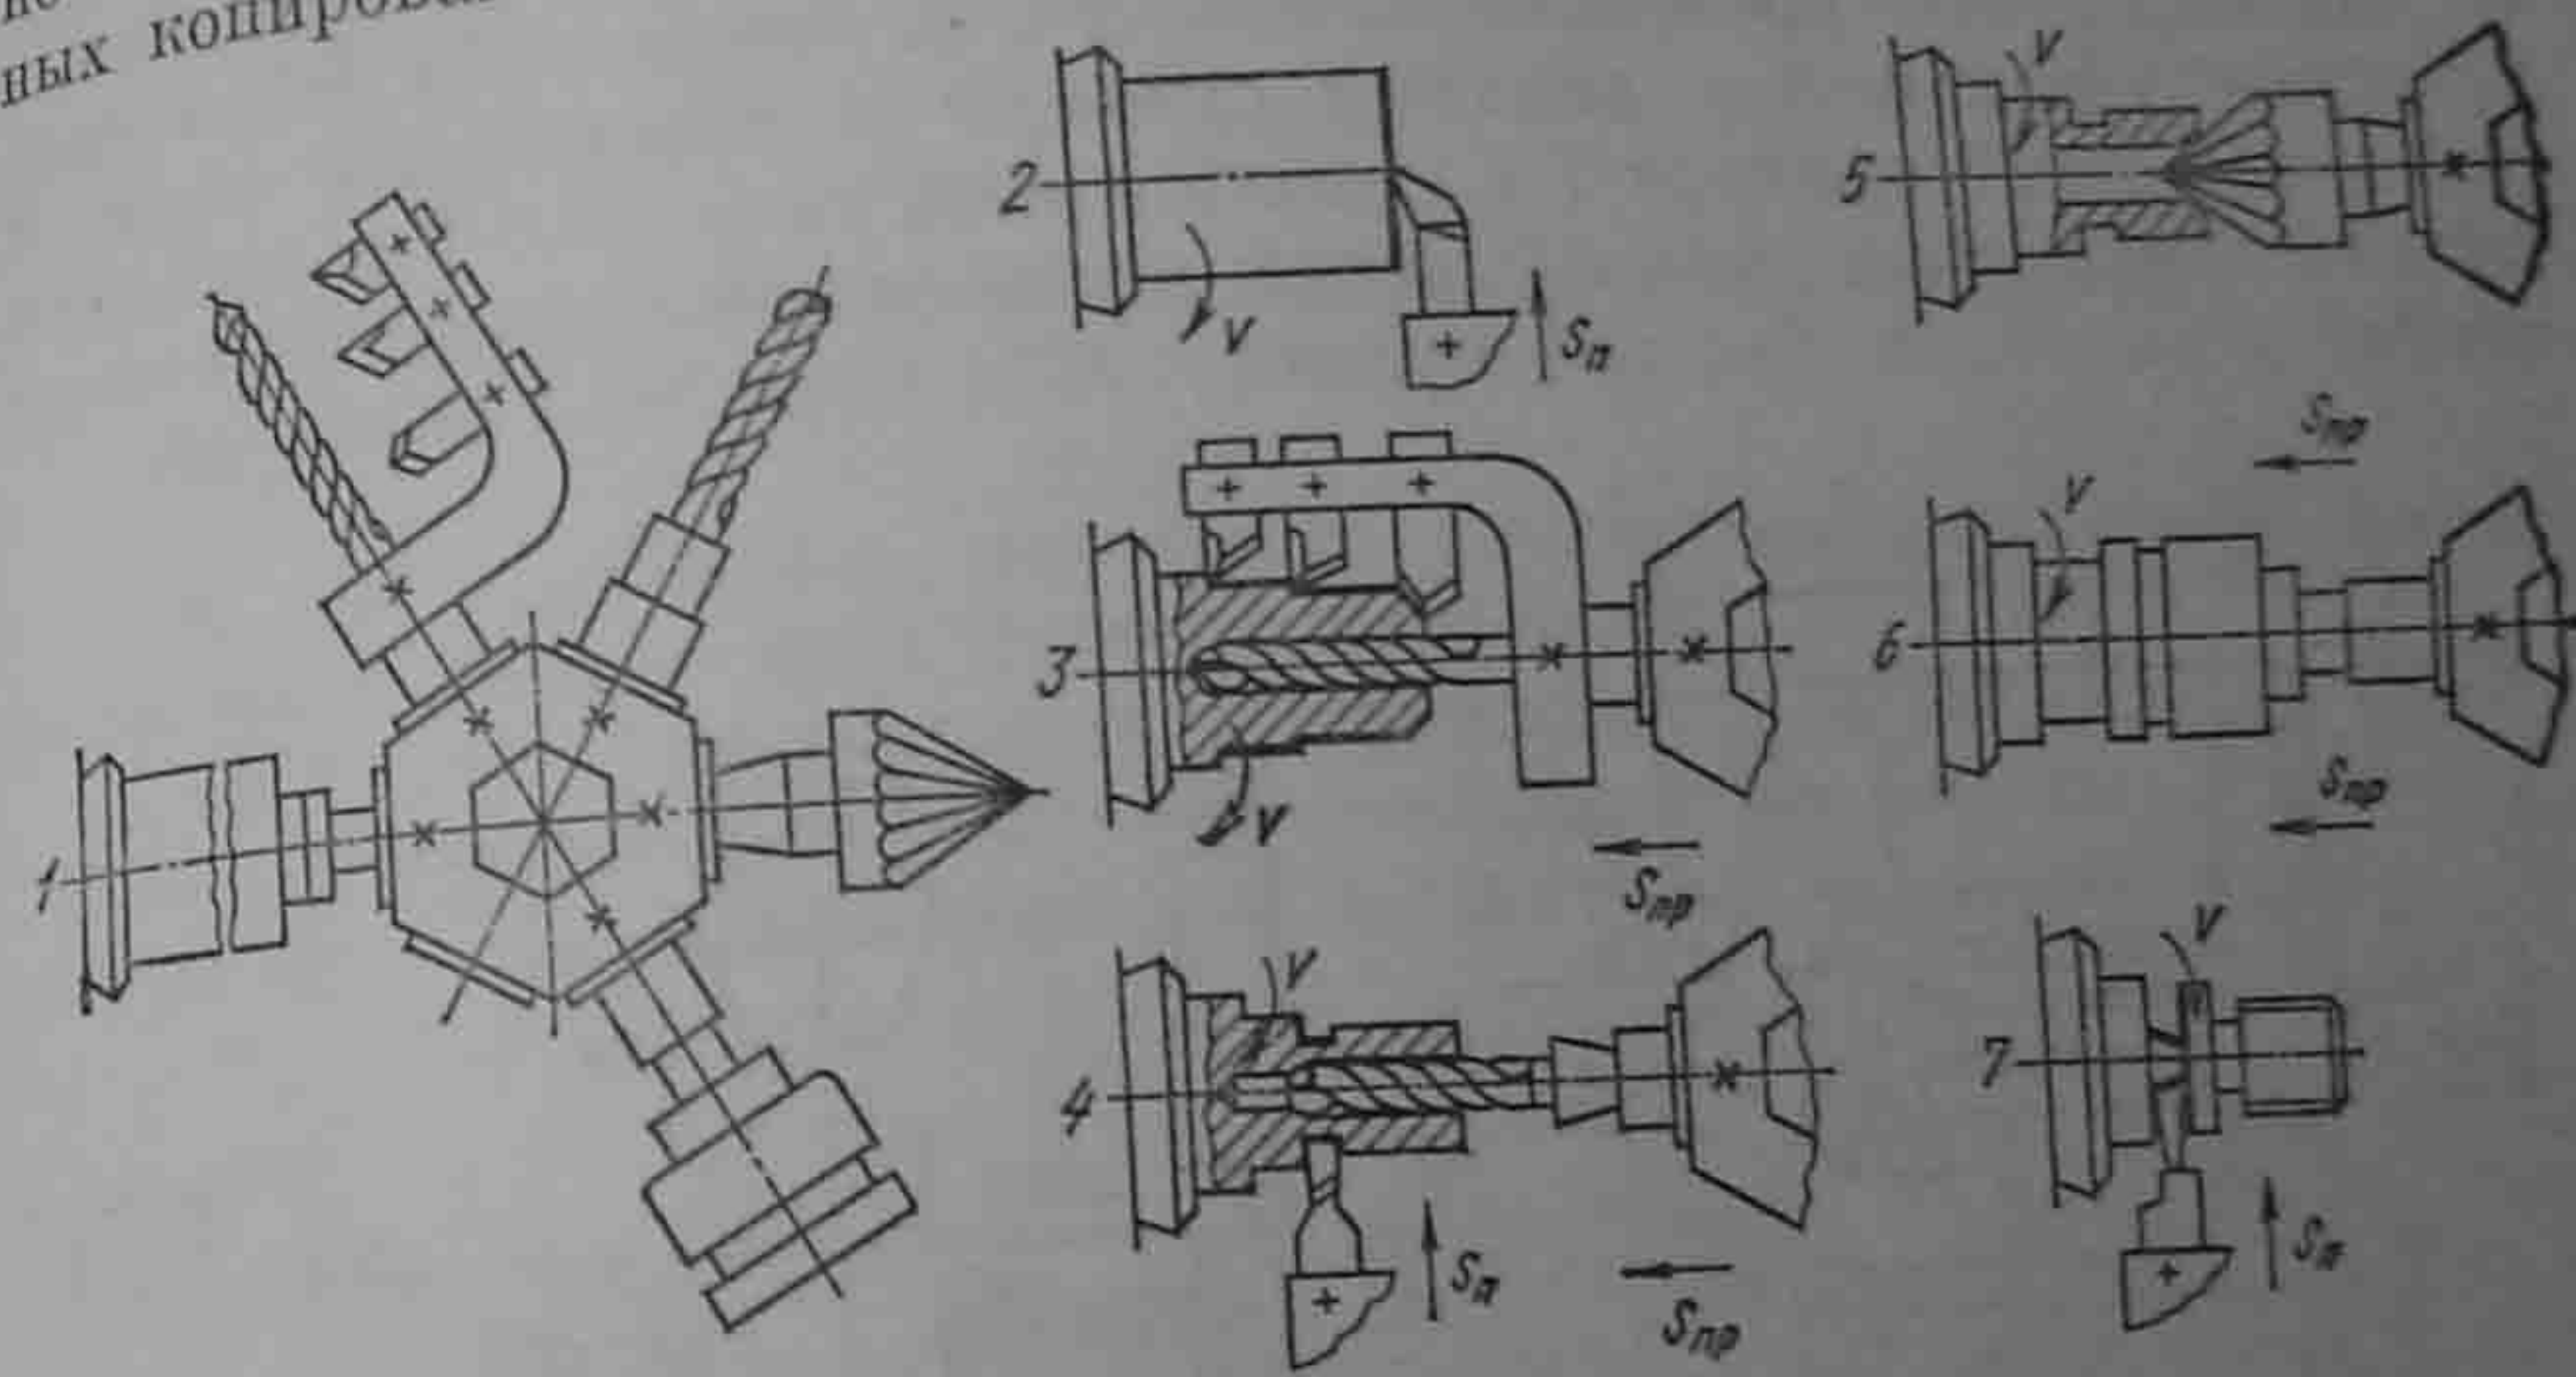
Схемы обработки поверхностей заготовки на токарно-револьверном станке: 1 — подача прутка до упора; 2 — подрезание правого торца; 3 — обтачивание двух цилиндрических поверхностей, снятие фаски и сверление отверстия; 4 — зенкерование отверстия и протачивание кольцевой канавки; 5 — зенкование; 6 — нарезание резьбы; 7 — отрезание детали
